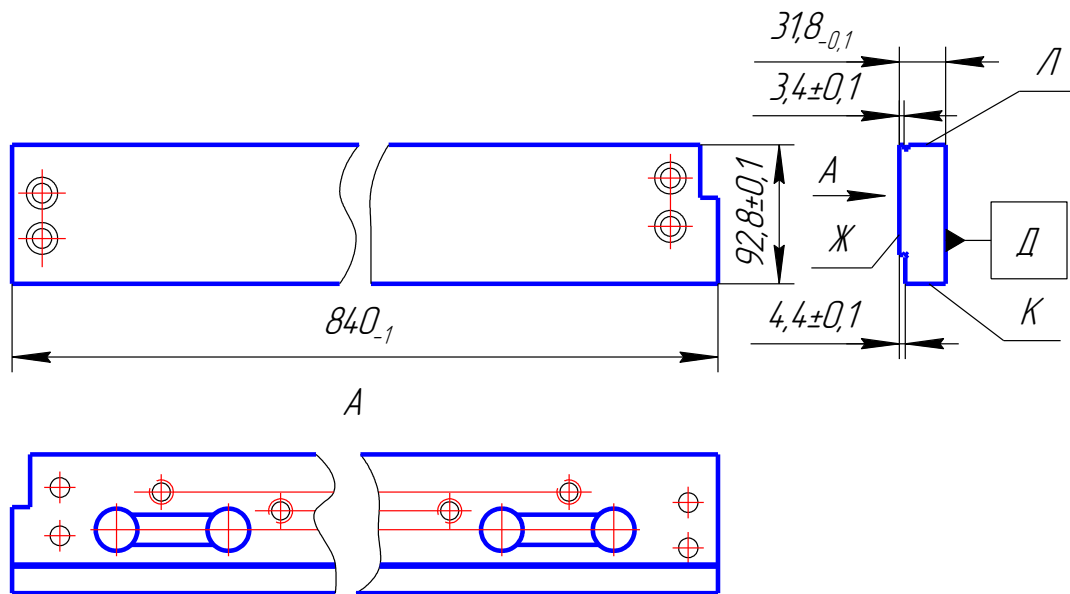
Заготовка планки ОММ64.70.00.00.011/24.101 для комбінованої обробки
